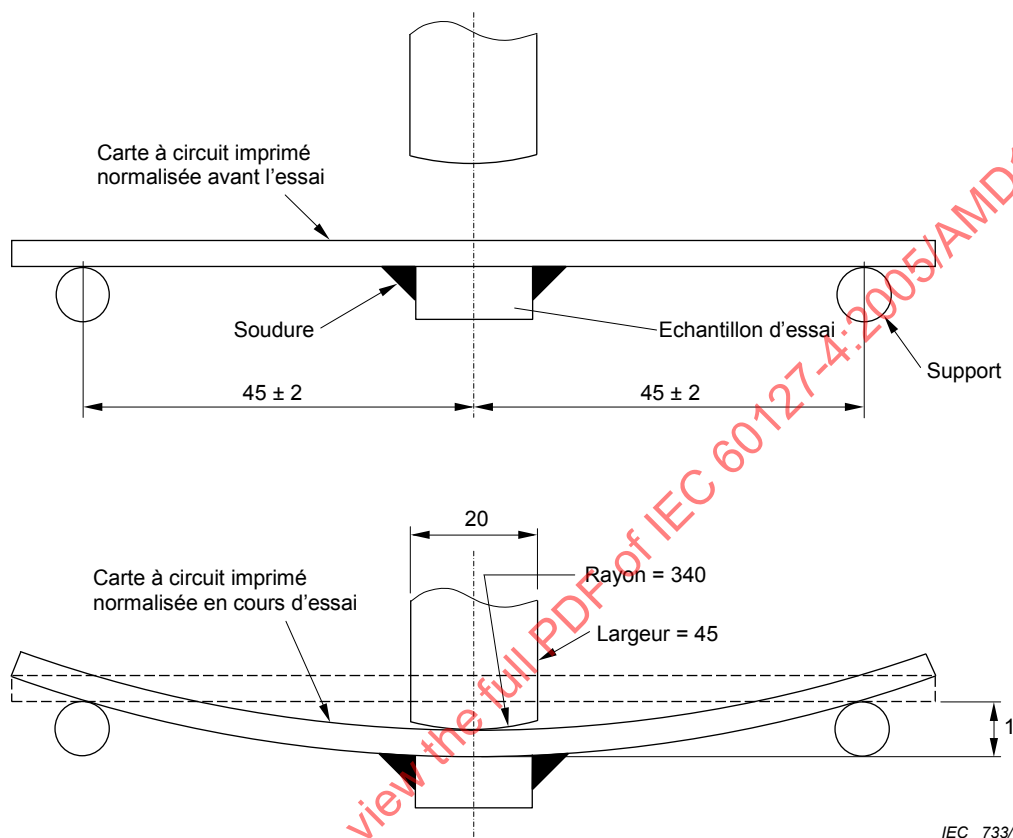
Carte d'essai à circuit imprimé pour éléments de remplacement à montage en surface
